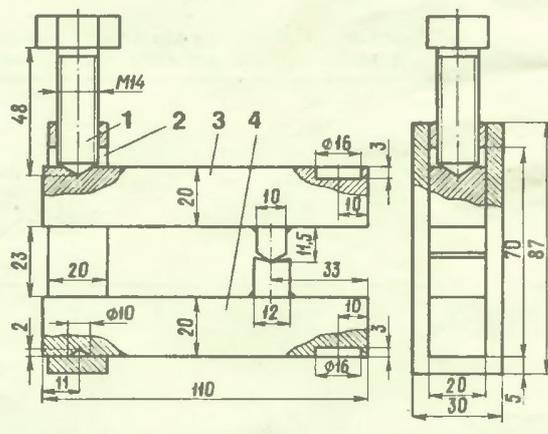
Приспособление Н. Сербина для выпрессовки шаровых шарниров из поворотного кулака в подвеске «Жигулей»: 1 — болт М14; 2 — хомут (материал ст. 3); 3 — верхний рычаг; 4 — нижний рычаг (материал рычагов ст. 40 или ст. 50).
